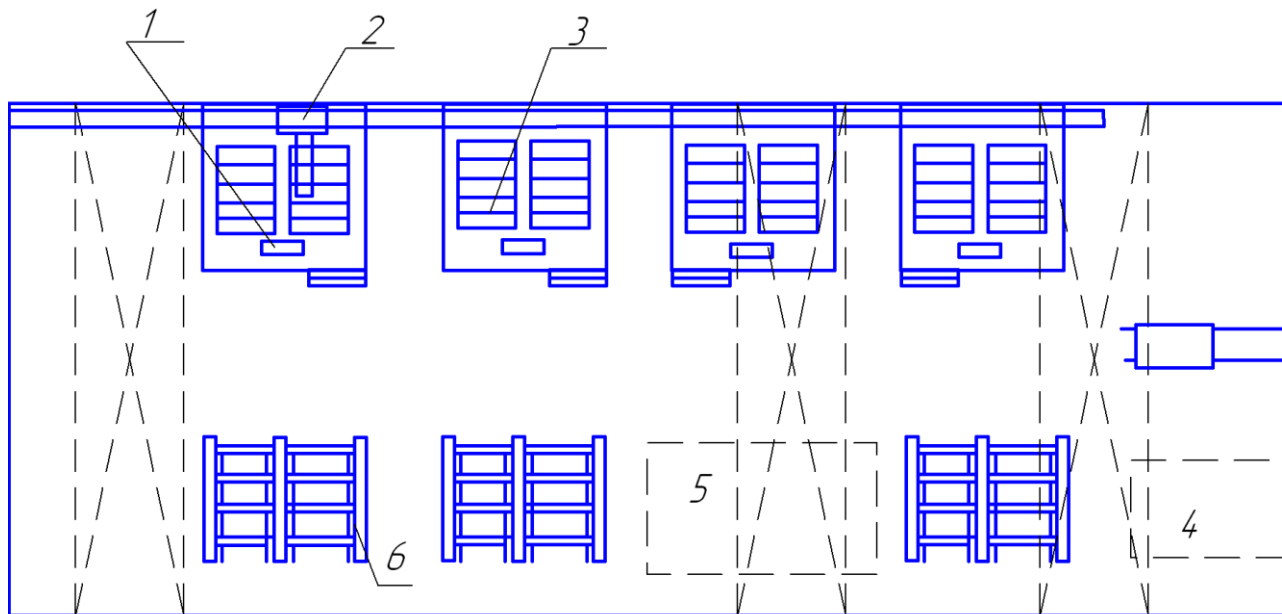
Схема кассетного производства панелей внутренних стен, перегородок и панелей перекрытия:
